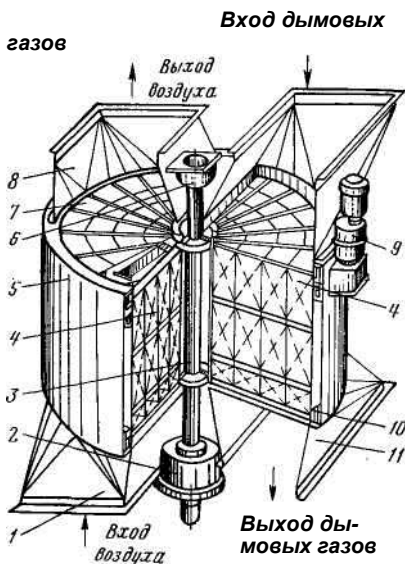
Регенеративный воздухоподогреватель с вращающейся насадкой:
